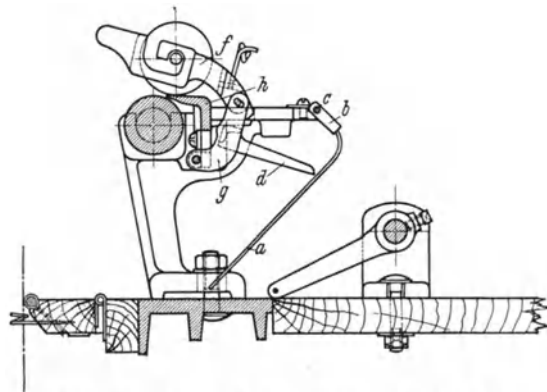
Oberzylinderabstellung für Zwirnmachines, eingerückt.
